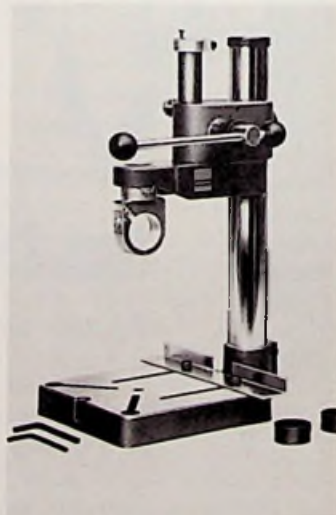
Universeller Bohr- und Fräsständer (Brennenstuhl)
